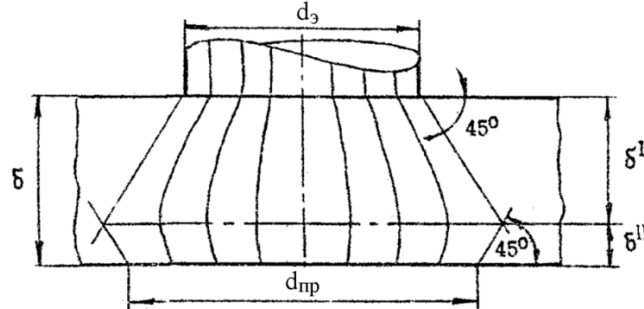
Схема поля тока для расчета сопротивления детали
